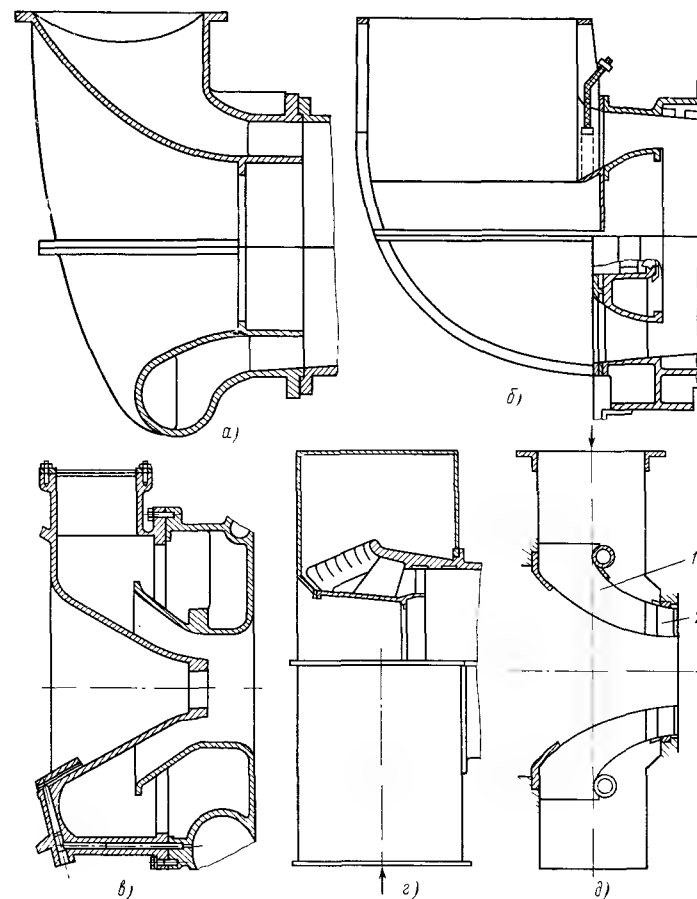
Входные патрубки компрессоров с радиальным подводом:
